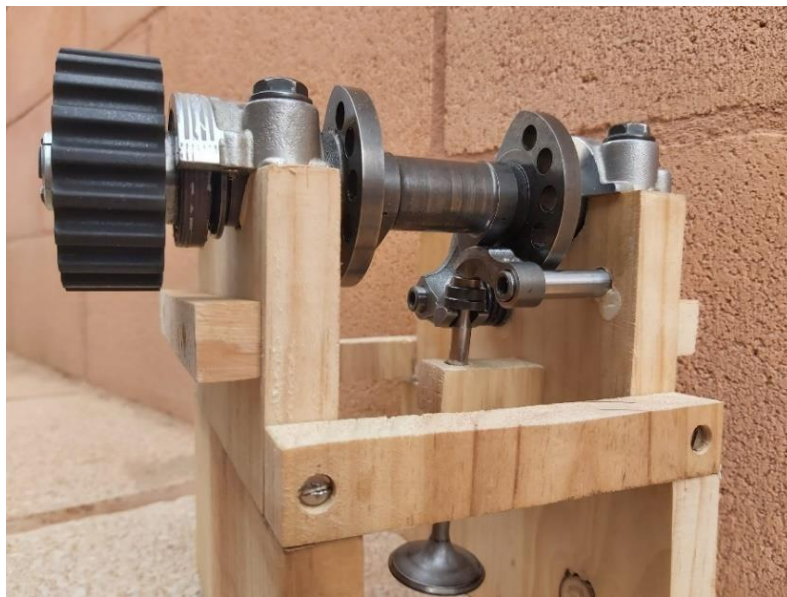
Vista perfil del ensamblaje. Fuente: Propia
